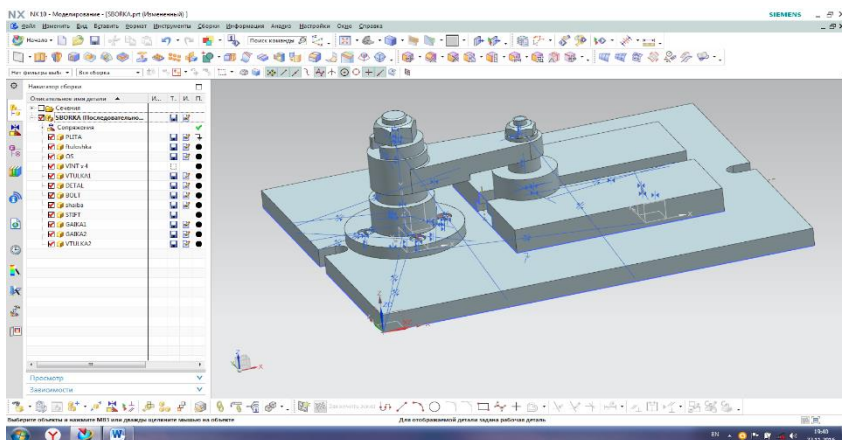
Перестроенная сборка с размерами детали  $A1=22$ ,  $A2=10$ ,  $L=95$
